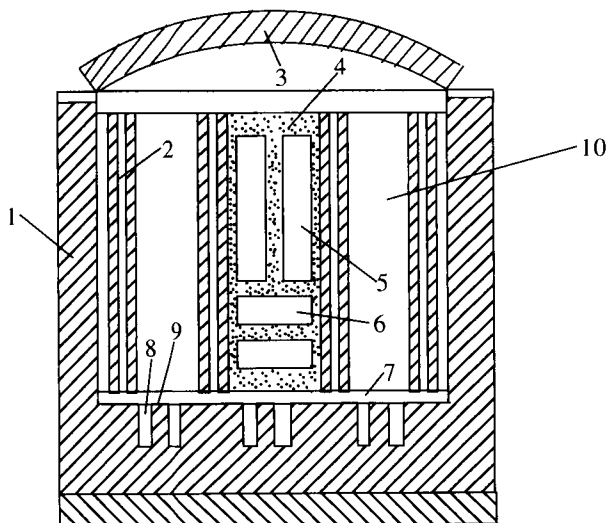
Продольный разрез камеры обжиговой печи:
